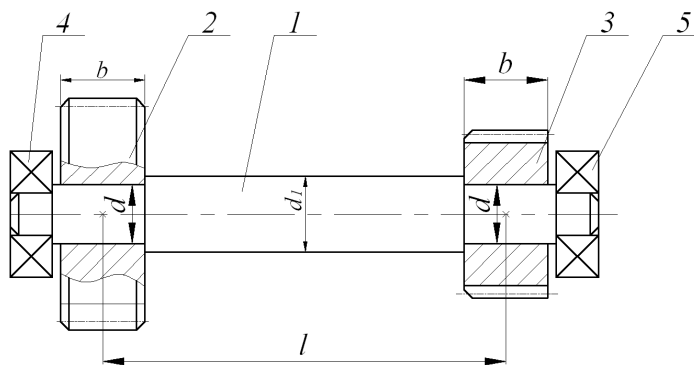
Конструктивна схема проміжного вала редуктора із напесованими на нього зубчатими колесами:
